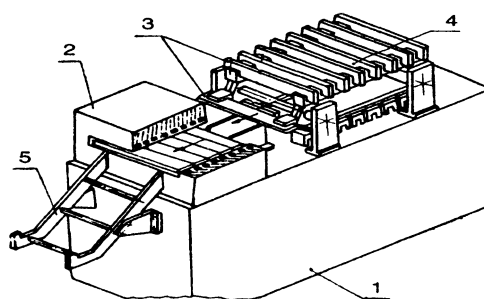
Установка для индукционного нагрева заготовок типа пластин: 1 — конденсаторный блок; 2 — индуктор; 3 — нагреваемая заготовка; 4 — накопитель; 5 — лоток выгрузки
